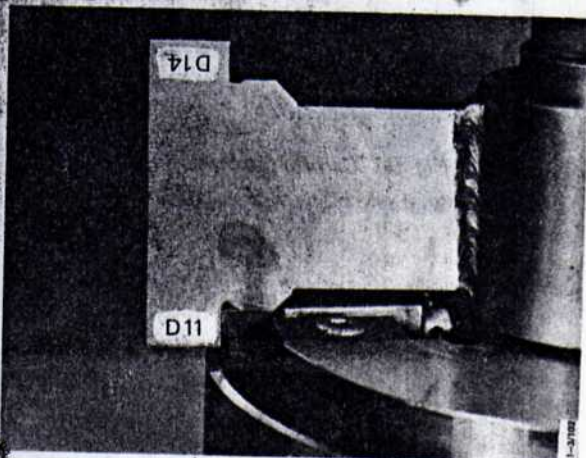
Herramienta de ajuste para el cortador del escariador de camisa
